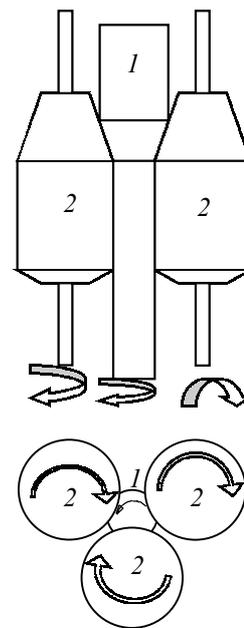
Обкатка круглой заготовки (1) тремя вращающимися роликами (2).
